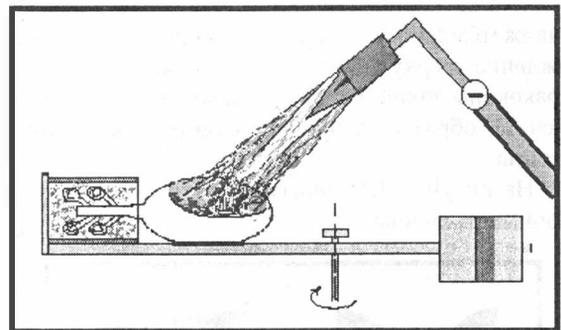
Схема плавки металла открытым пламенем при центробежном литье
